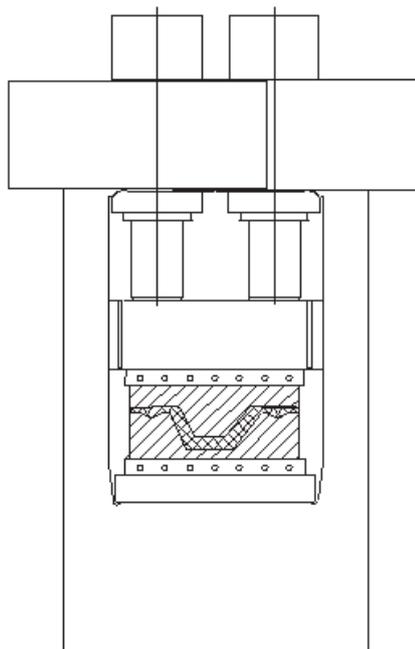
Presse zum Formpressen mit geschlossenem Werkzeug und mit ausgeformter Formmasse
